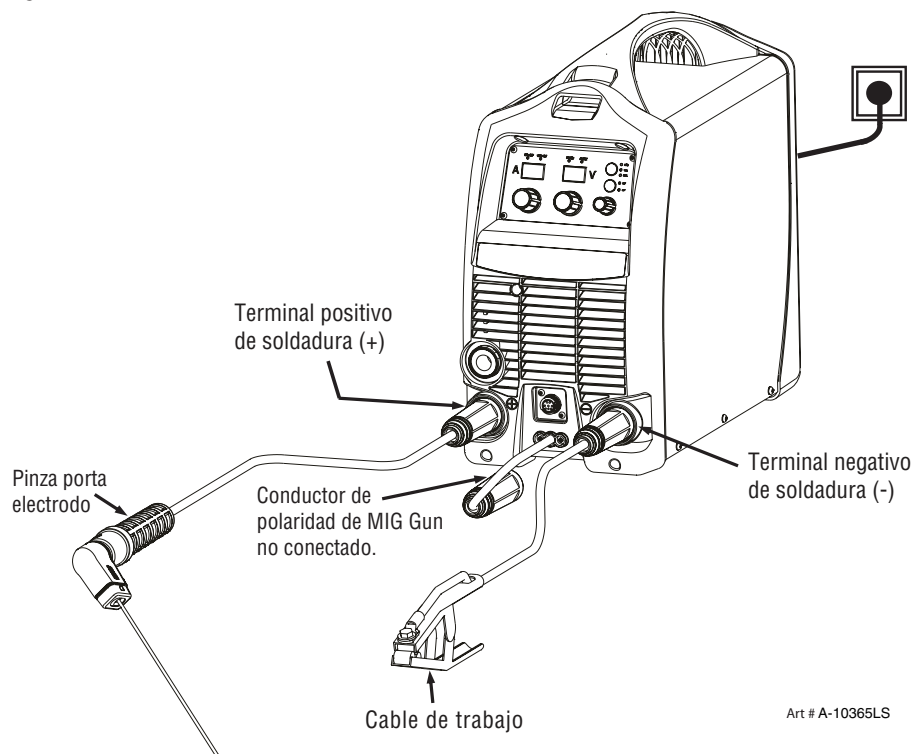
Configuración para la soldadura por arco manual
